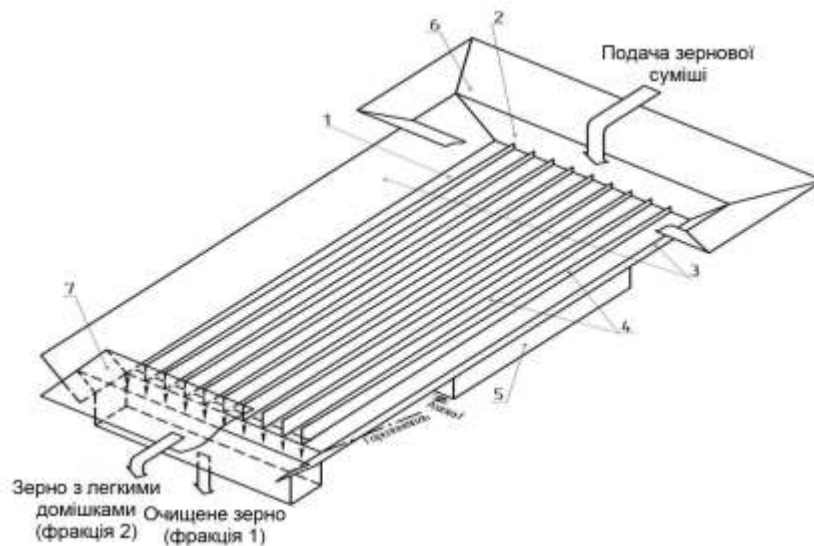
Схема робочого органу: 1- робочий орган; 2-торцева стінка; 3- бічні стінки; 4- рифлі; 5- привід; 6 - живильник; 7- ніж.
